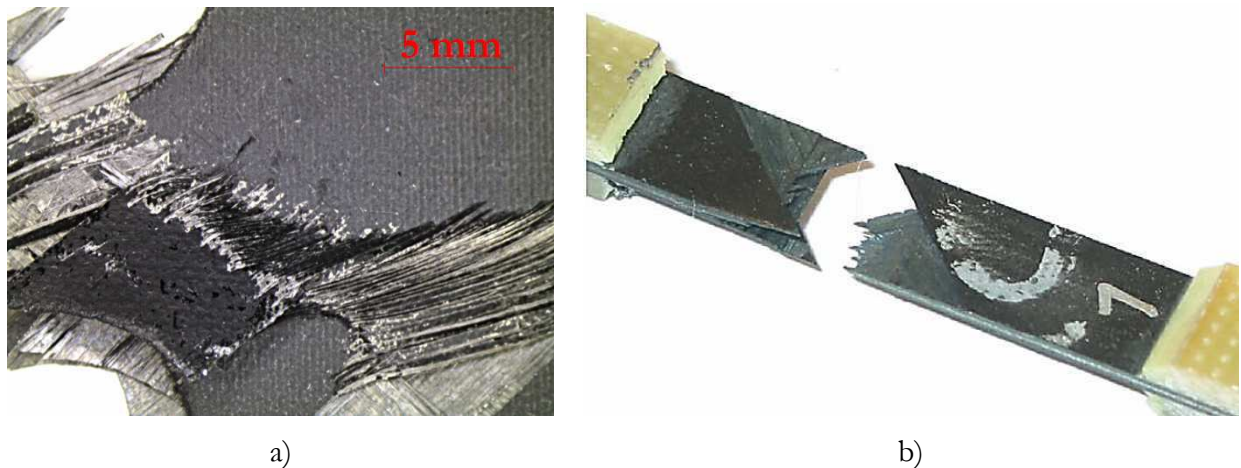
a) Rupture de l'éprouvette entaillée bobinée. b) rupture d'une éprouvette stratifiée.
